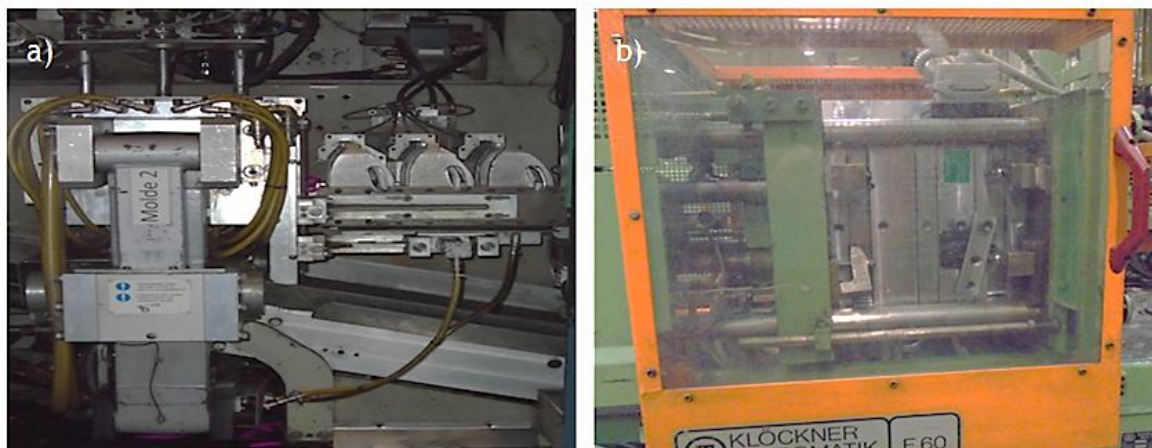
Linhas de fabrico de embalagens plásticas: a) sopro e b) injeção.
